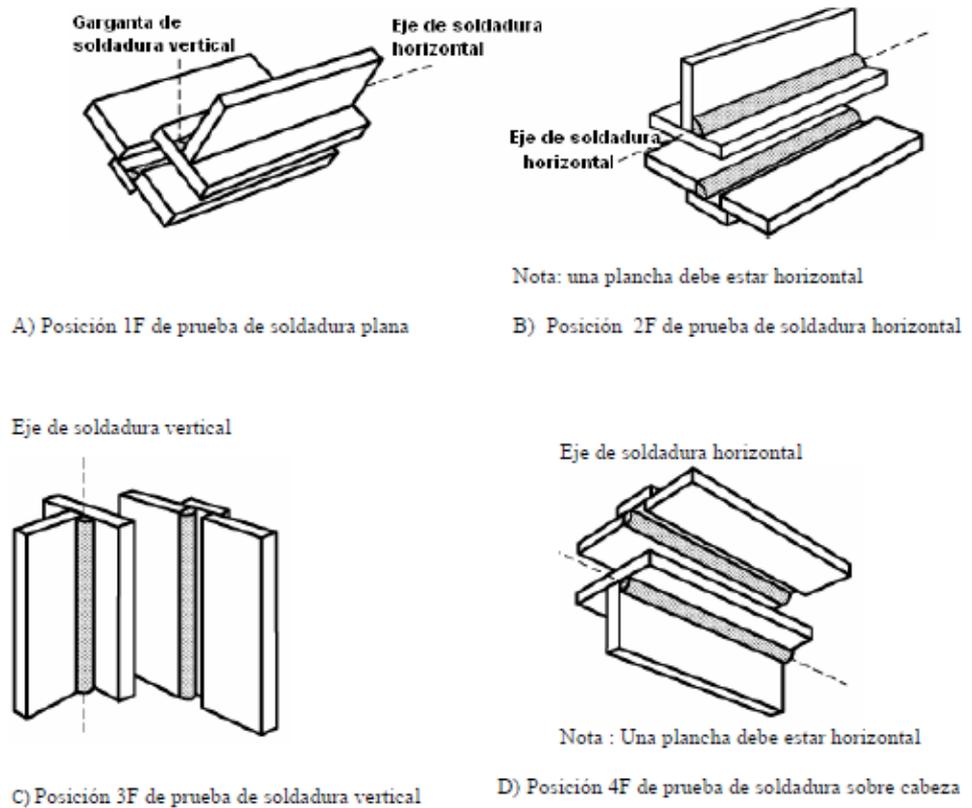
POSICIONES DE PLANCHAS DE PRUEBAS PARA SOLDADURAS DE FILETE. [12]
